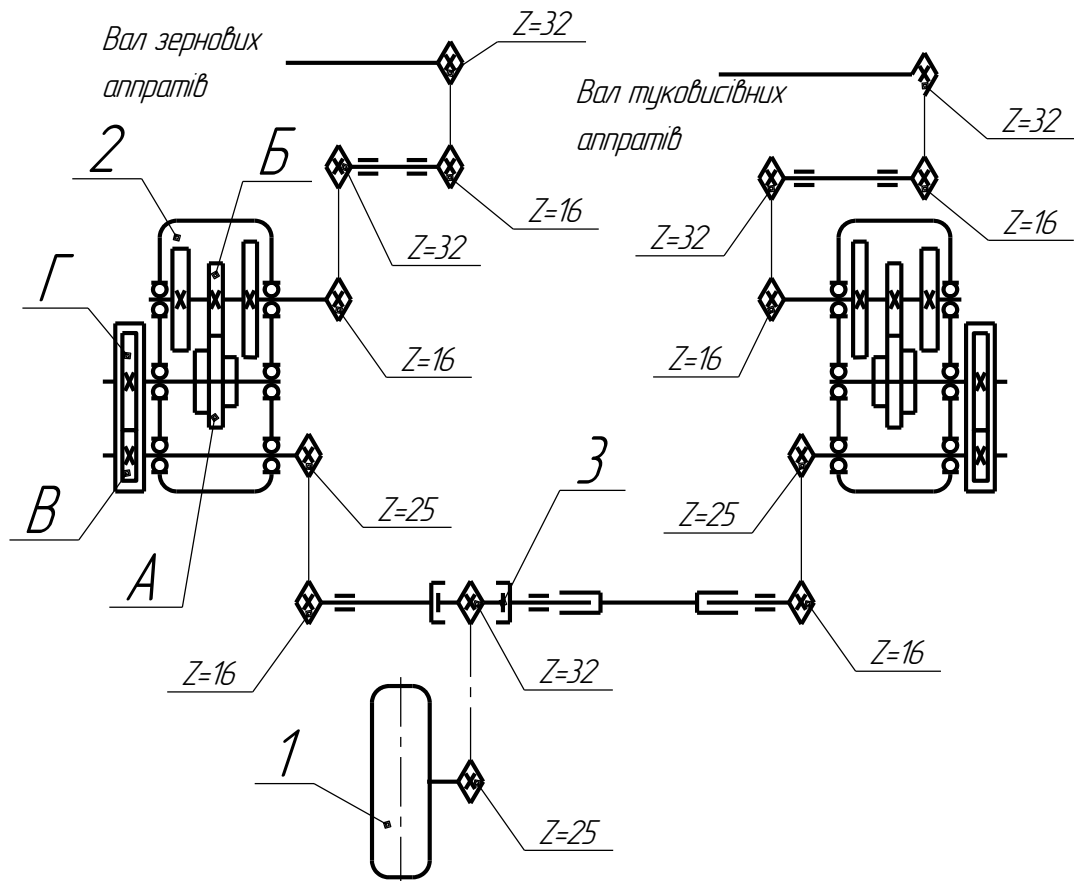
Схема механізму передач: 1- опорно-приводне колесо;
